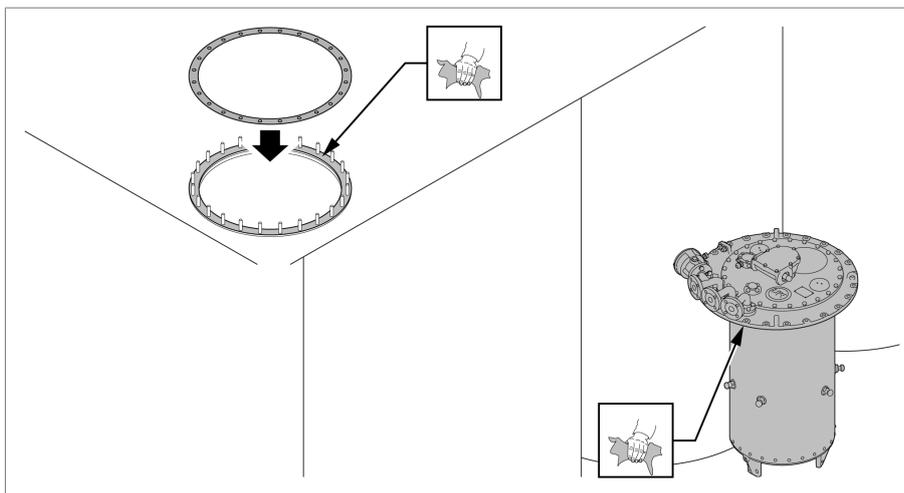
Surfaces d'étanchéité, joint d'étanchéité
